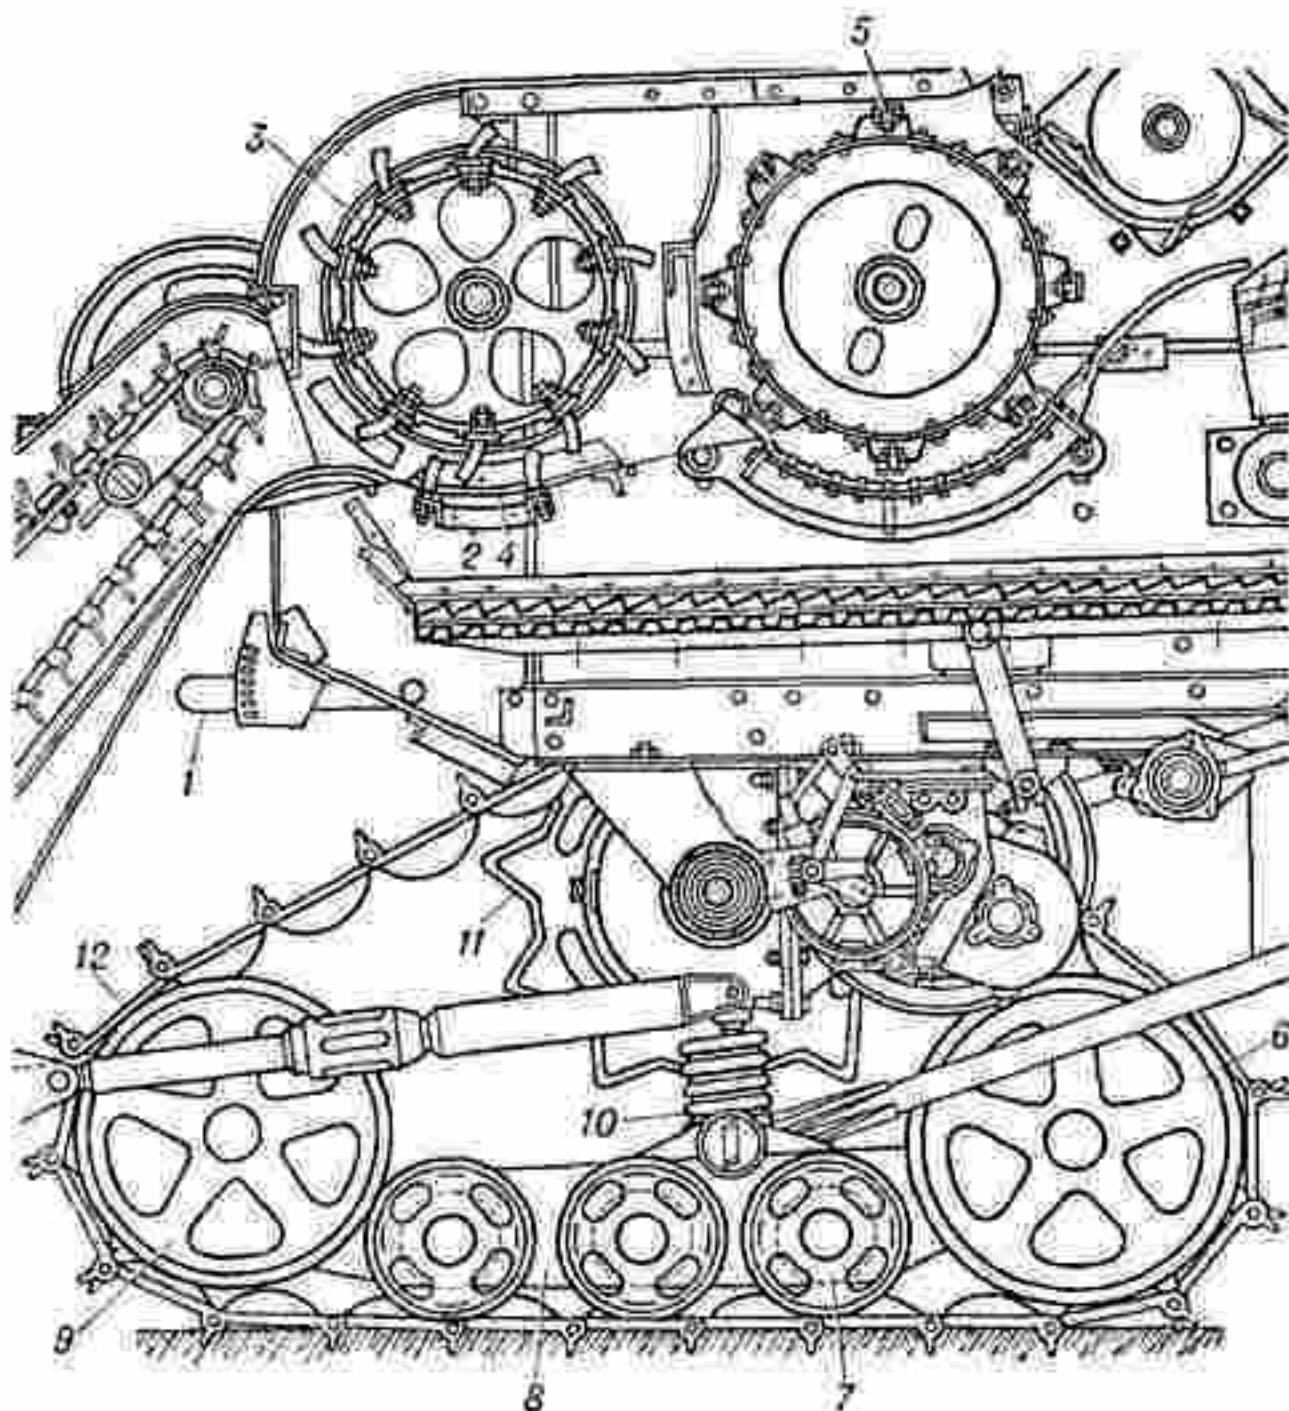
Молотильное устройство и гусеничный движитель комбайна для уборки риса на переувлажнённых почвах: 1 — рычаг для регулирования зубовой рамки; 2 — зубовая рамка; 3 — штифтовый барабан; 4 — решётка; 5 — бильный барабан; 6 и 9 — направляющие колеса; 7 — каток; 8 — балансирующая тележка; 10 — амортизатор; 11 — ведущая звездочка; 12 — гусеничная лента.
